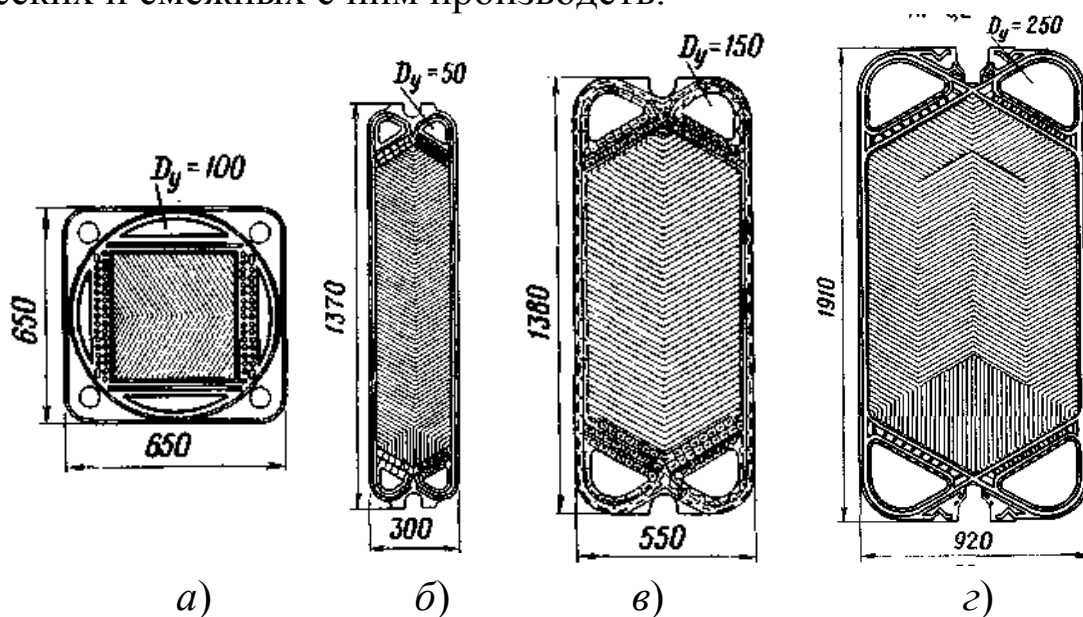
Конструкция сетчато-поточных пластин для выпуска широкого размерного ряда теплообменных аппаратов:
